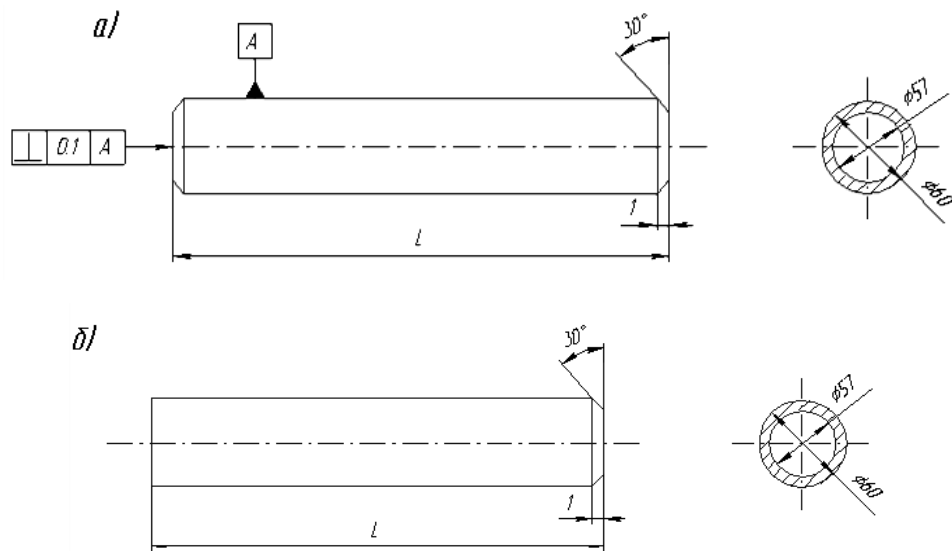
Схема вирізання заготовок труб для стінки котла
